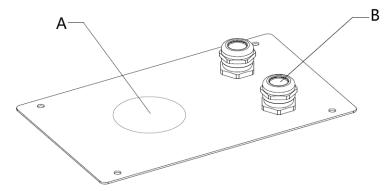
Guider les câbles à travers la plaque passe-câble
